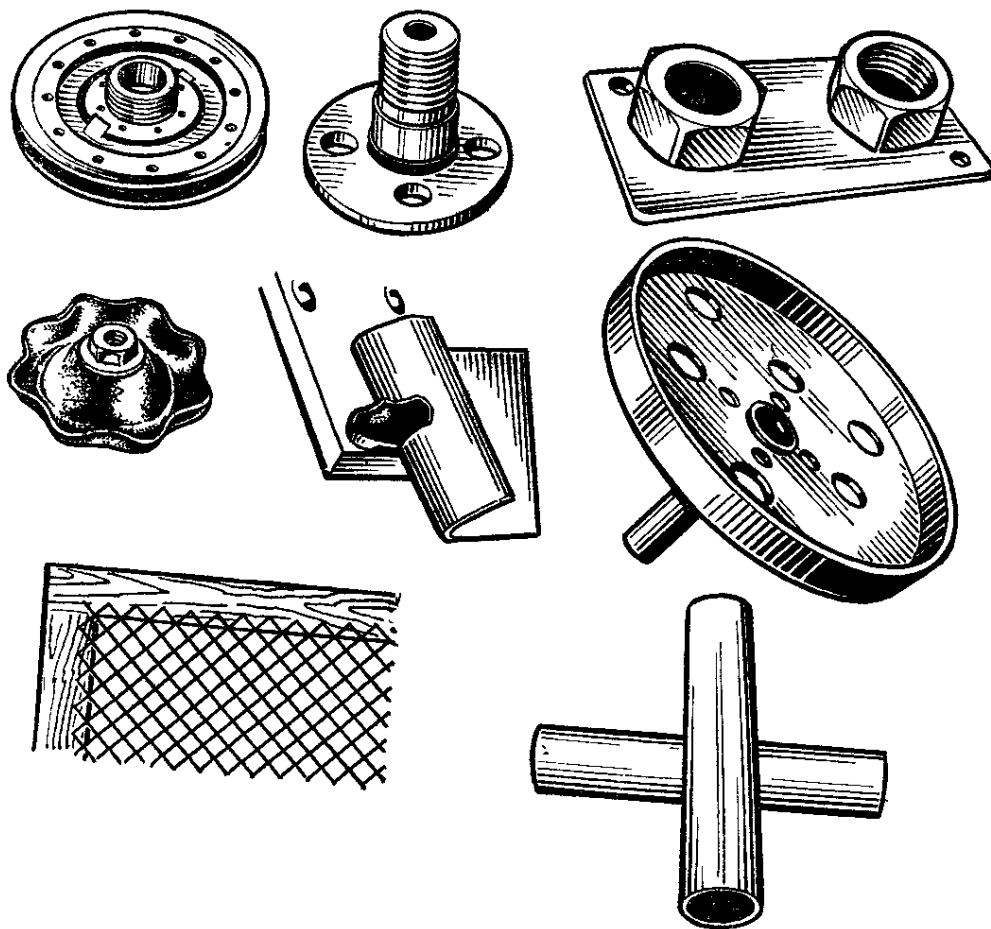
Детали, сваренные рельефной сваркой
